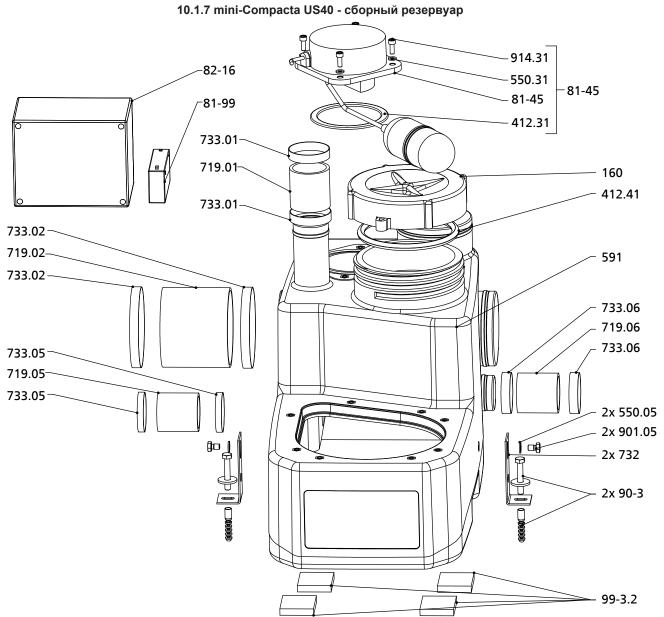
Покомпонентный сборочный чертеж mini-Compacta US40 — сборный резервуар
